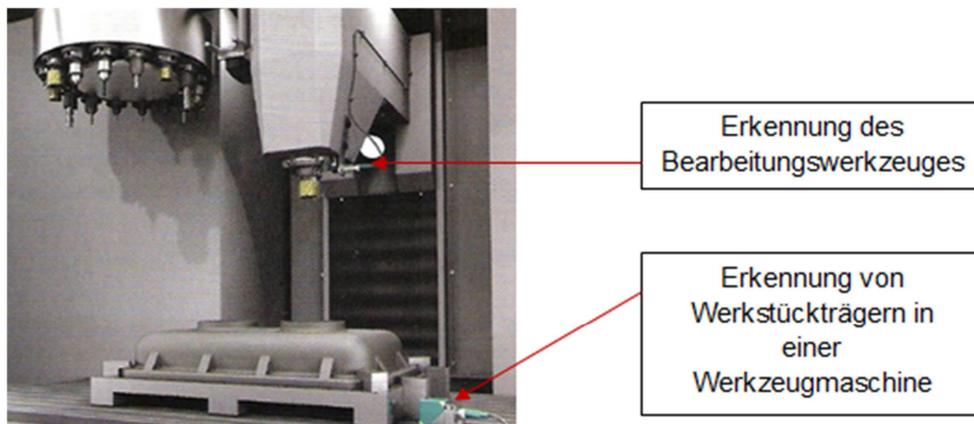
Einsatz von RFID-Technik in Werkzeugmaschinen [37]
